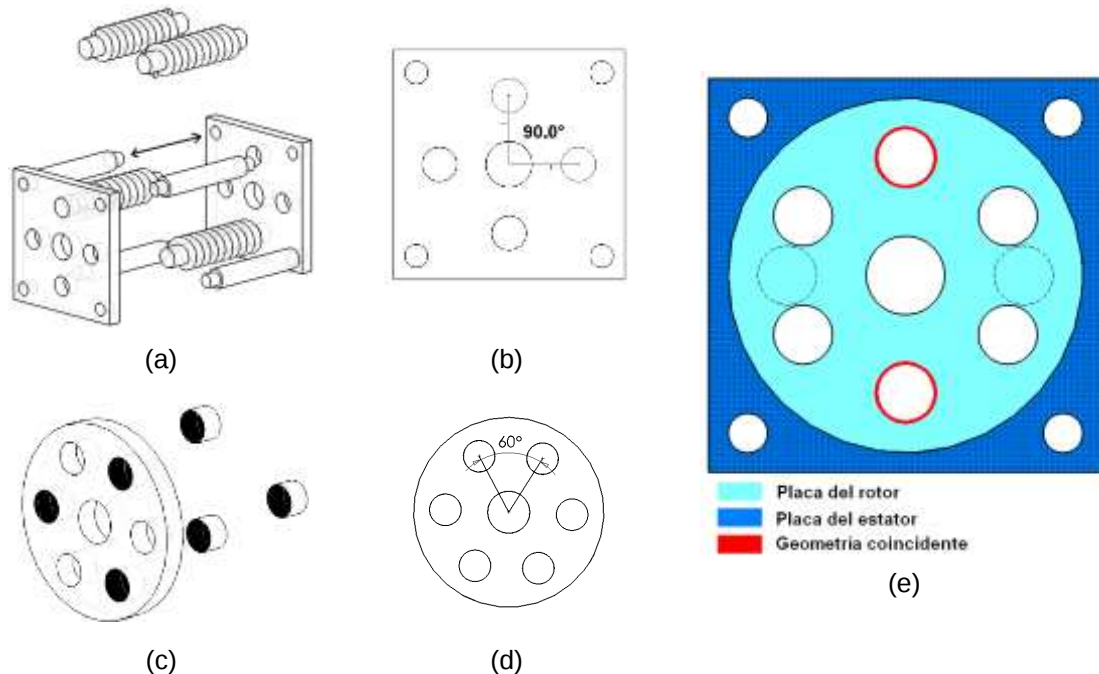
Estator y rotor. (a) Armado del estator. (b) Vista frontal de la placa del estator. (c) Armado del rotor. (d) Vista frontal del rotor. (e) Coincidencia geométrica ambas partes.
